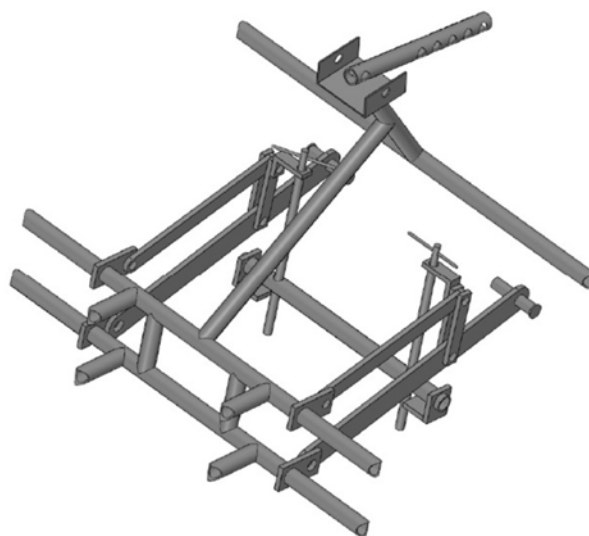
Maquete eletrônica do acoplamento projetada no software de CAD SolidWorks.
